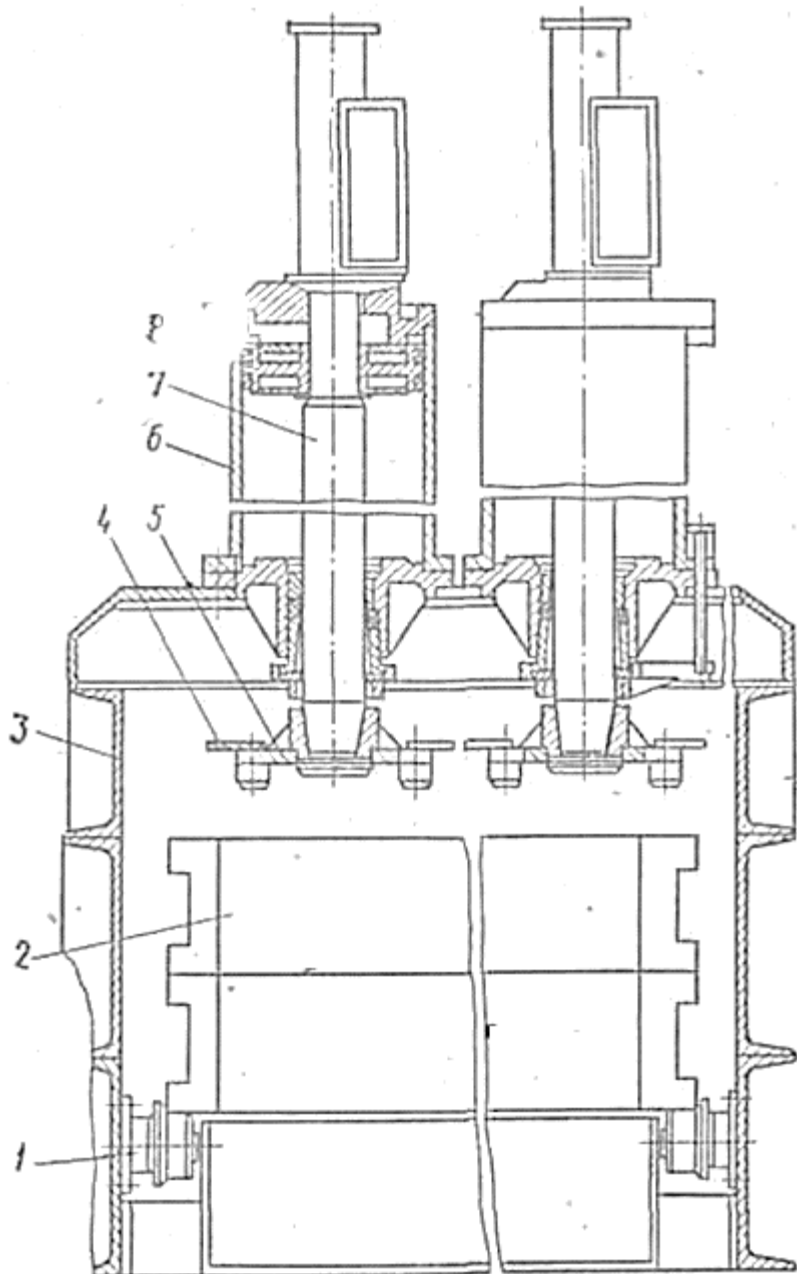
Установка для выдавливания горелого кома с отливкой из опок: 1 – рольганг; 2 – форма; 3 – рама; 4 – резиновые скребки; 5 – плита; 6 – пневмоцилиндр; 7 – шток; 8 – поршень
